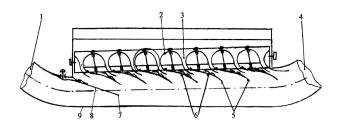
Схема загрузочного устройства для транспортирования зерна в бункер зерноуборочного комбайна:
